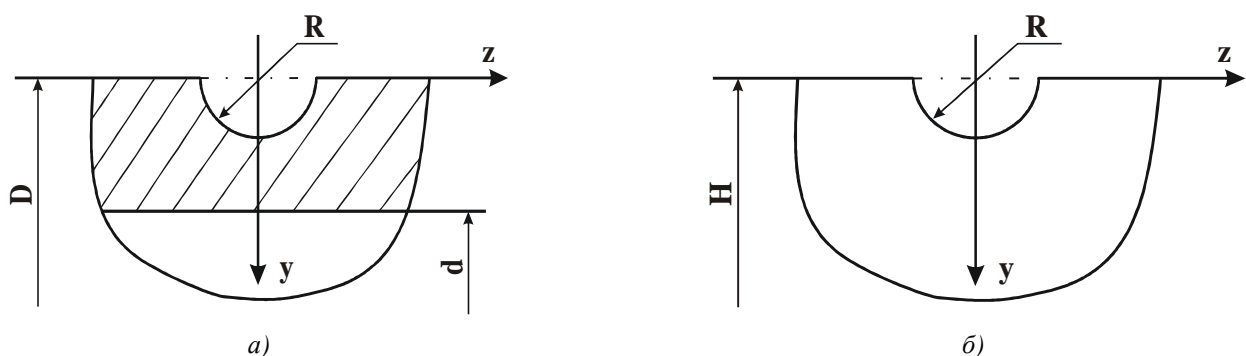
Надрез полукруглого профиля на цилиндрической детали (а) и детали прямоугольного поперечного сечения (б)
